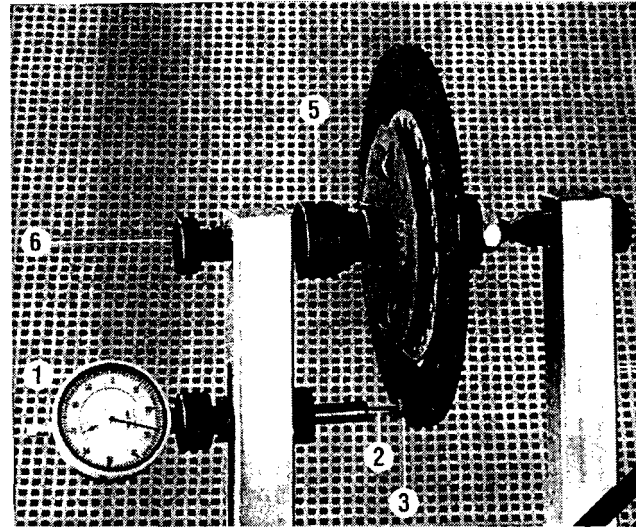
Проверка биения рабочей поверхности ведомого диска.
